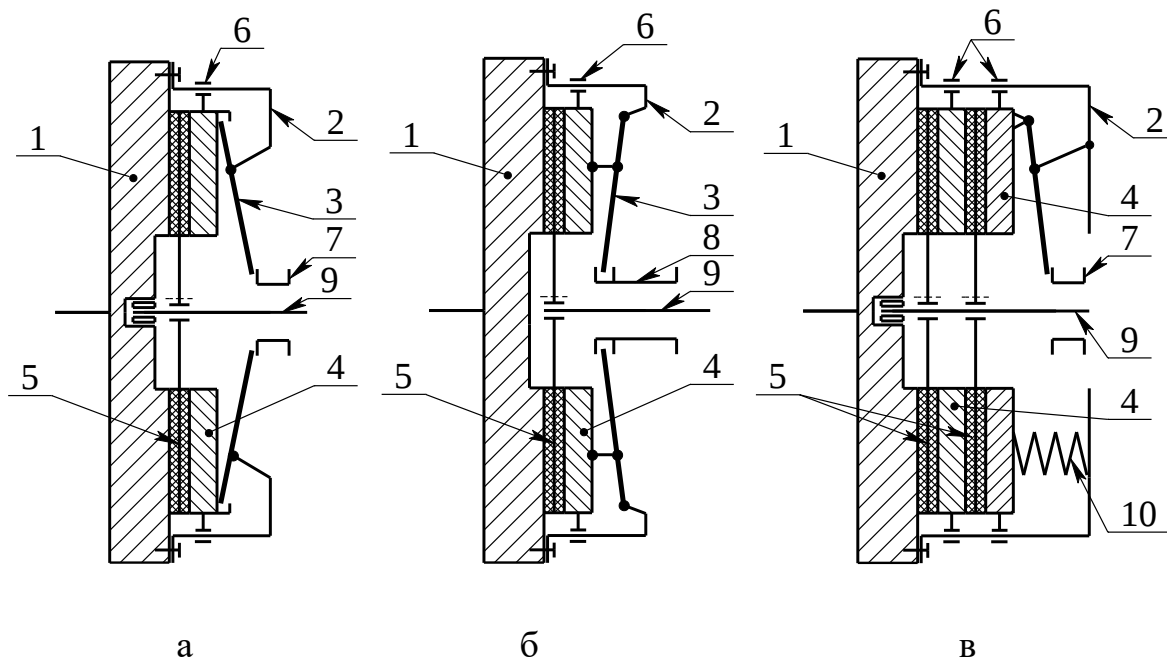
Кінематичні схеми зчеплень: а, б – зчеплення з діафрагмовою пружиною; в – зчеплення з периферійно розташованими циліндричними пружинами; 1 – маховик двигуна; 2 - кожух; 3 – діафрагмова пружина; 4 – натискний диск; 5 – ведений диск; 6 – напрямні пристрої натискного та проміжного дисків; 7, 8 – муфта вимкнення зчеплення відповідно натискна та витяжна; 9 – первинний вал коробки передач; 10 – циліндрична пружина
